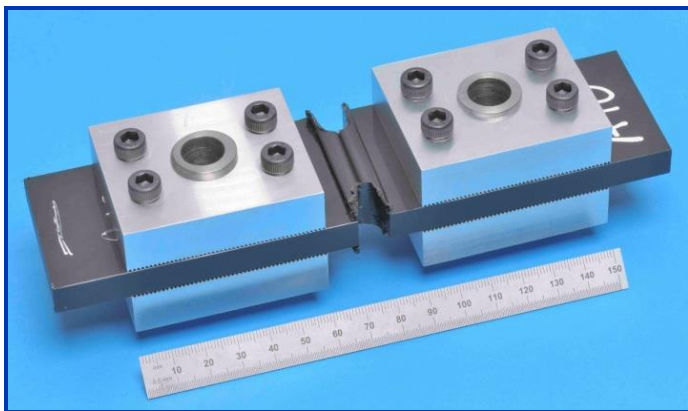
PROBETA DE UN ENSAYO DE TRACCIÓN EN SOLDADURAS BF.
